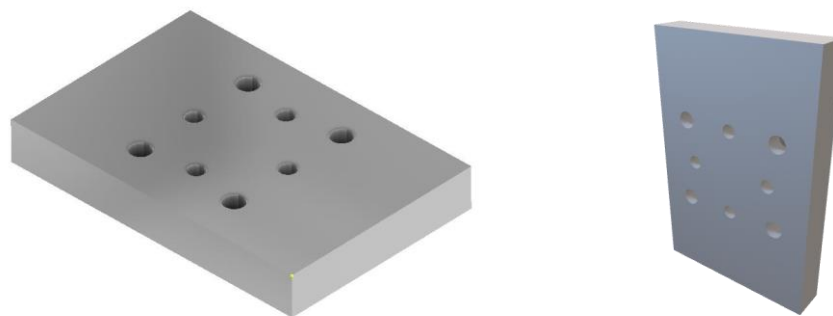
Τρισδιάστατη απεικόνιση αποστολής 26
